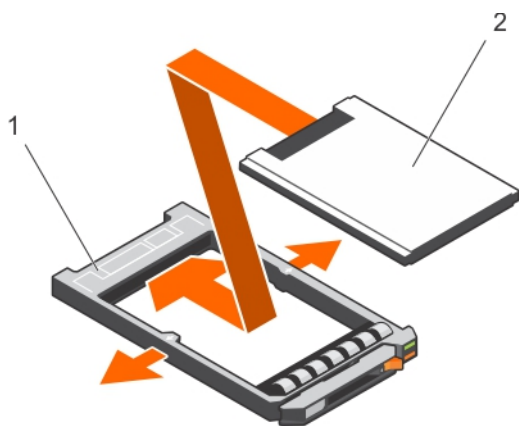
Installation d'un lecteur SSD de 1,8 pouce dans un support de SSD
